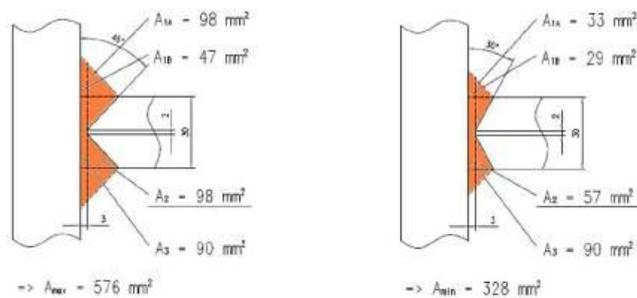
Т-образное соединение, выполненное односторонней сваркой, притупление 8 мм, сварочное волокно 30°, механизированная сварка, положение сварки РВ
